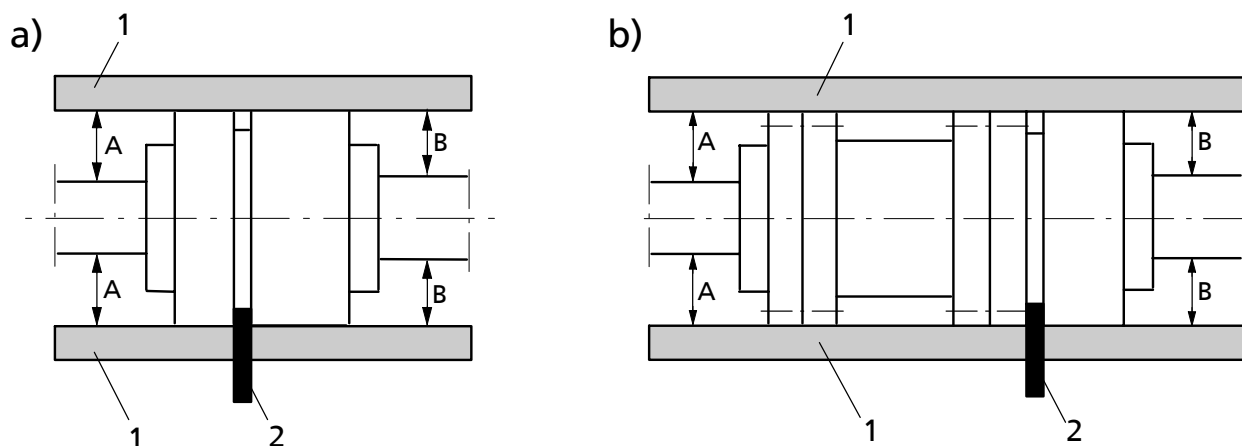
а) Контроль центровки муфты и б) центровка муфты с проставкой
